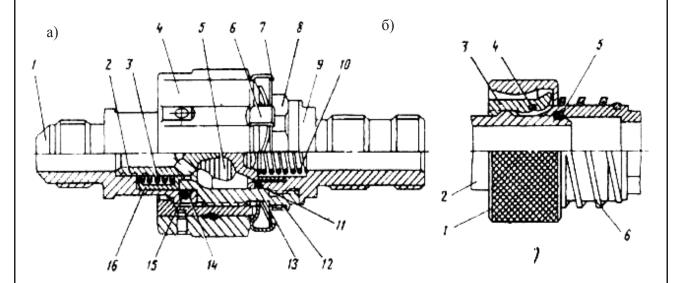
Схемы быстроразъемных неподвижных беспрокладочных соединений трубопроводов: а – разъемный клапан: 1 – штуцер; 2 – клапан; 3, 10 – пружины; 4 – гайка в сборе (гайка, обойма, штифт); 5 – клапан; 6 – пружина; 7 – контровочная шайба; 8 – корпус; 9 – штуцер; 11, 15 – уплотнительные кольца; 12 – обойма; 13, 14 – защитные шайбы; 16 – втулка; б – цангового типа: 1 – обойма; 2 – наконечник; 3 – кулачок; 4 – кольцо; 5 – уплотнительное кольцо; 6 – пружина
